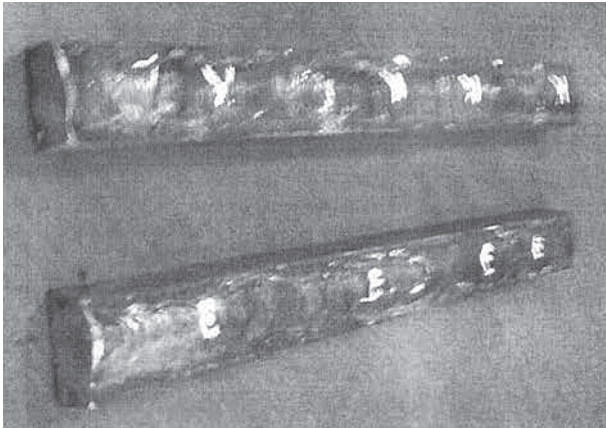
Заготовки для изготовления образцов на растяжение металла сварного шва
